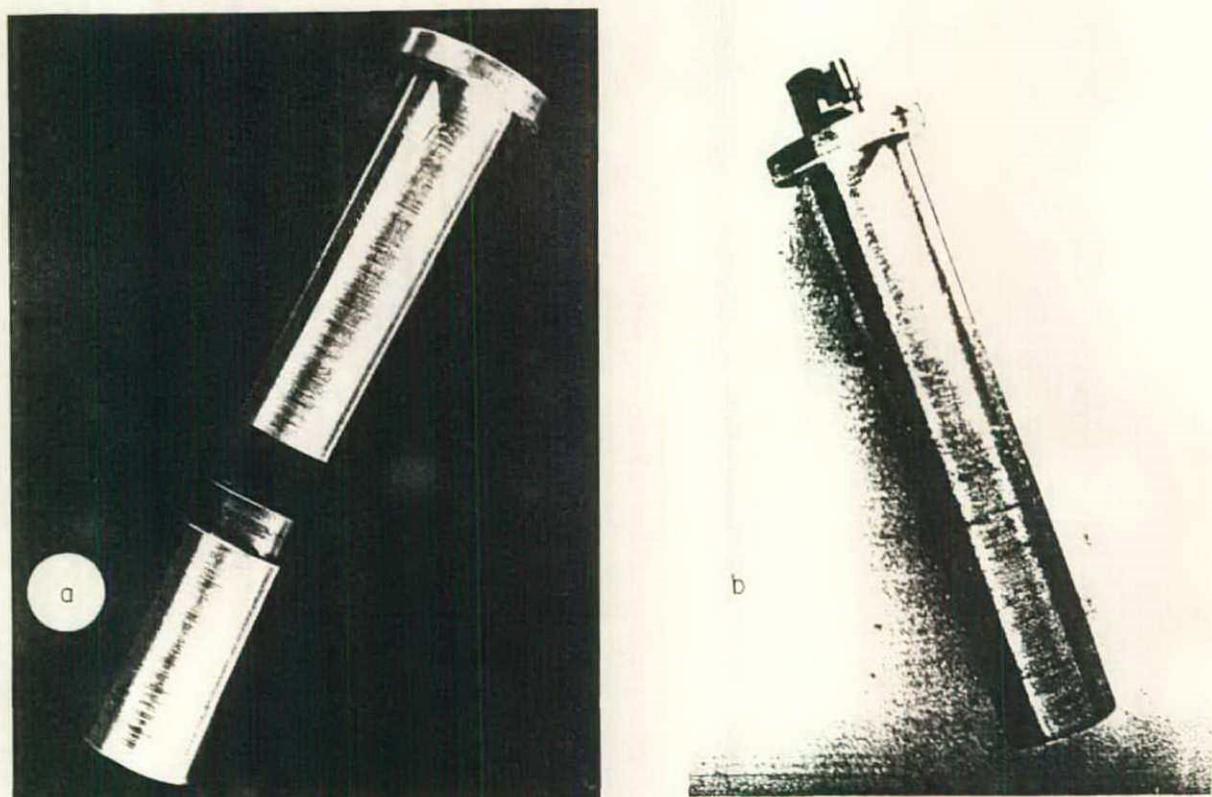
Estrutura de alumínio: a) desmontada; b) montada.
